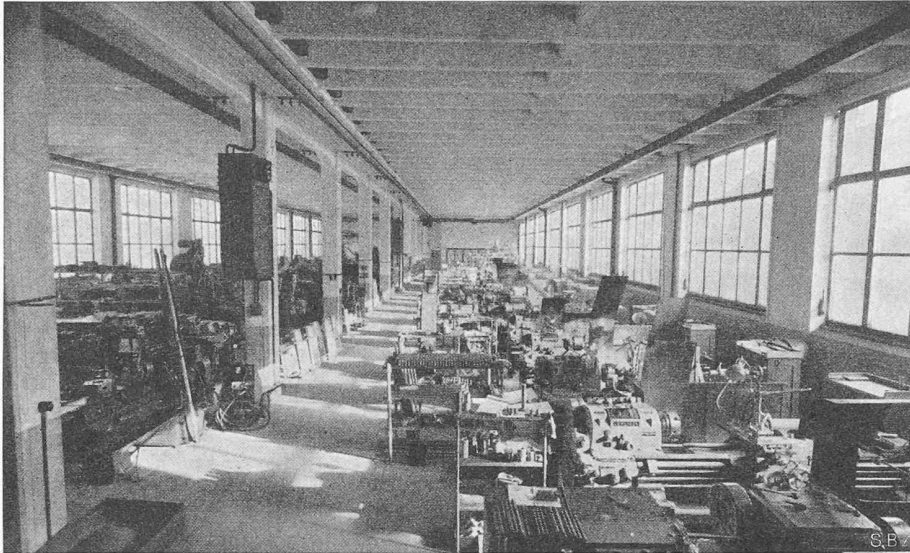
Zweiter Stock, Werkzeugmaschinenaal
